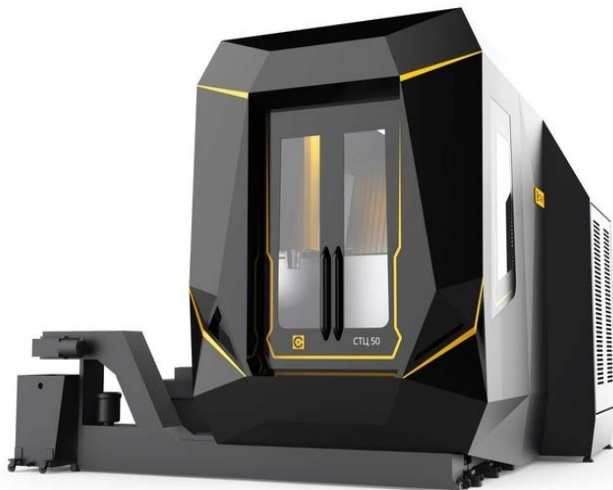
Фрезерный вертикальный обрабатывающий центр *S500U* (производитель ООО «НПО «Станкостроение» г. Стерлитамак)
